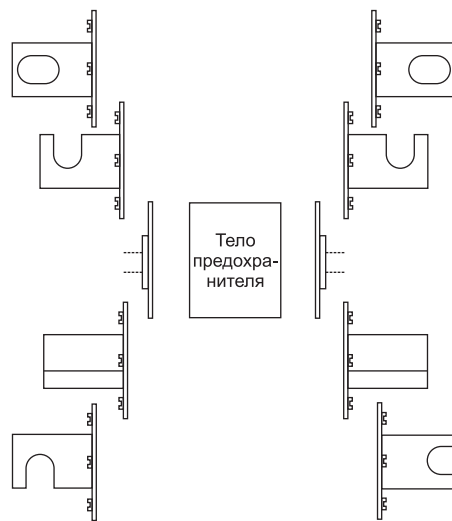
Стандарты предохранителей в прямоугольном корпусе с различным исполнением контактов
